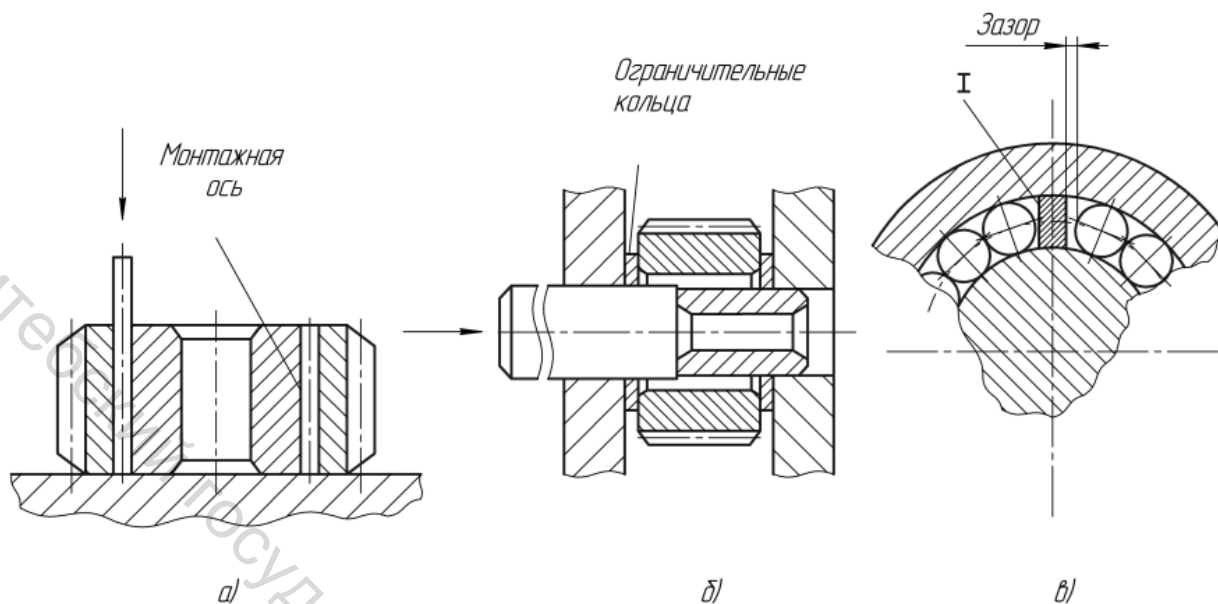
Сборка сборочных единиц с игольчатыми подшипниками
